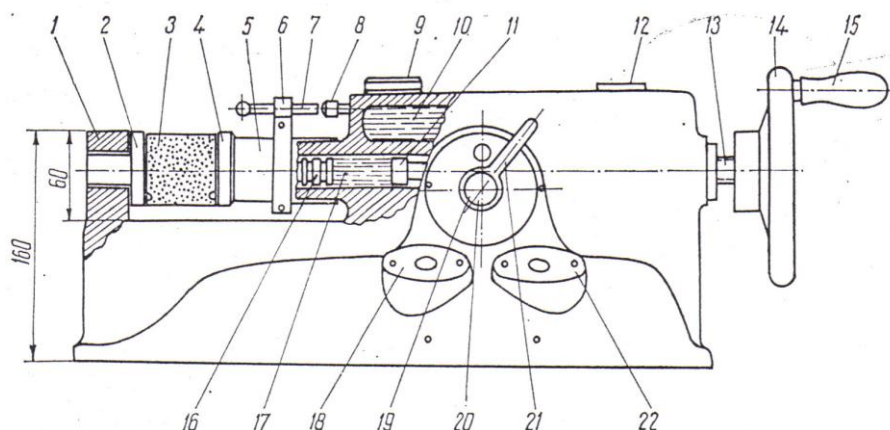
Aparat pentru încercări mecanice cu acționare hidraulică : 1-corpul aparatului ; 2-disc de sprijin ; 3-epruvetă cilindrică ; 4-disc disc de presare ; 5-piston exterior ; 6-brășară ; 7-tijă ; 8-tijă mobilă ; 9-comparator ; 10-rezervor de ulei ; 11-piston interior ; 12-dop ; 13- tija filetată ; 14-roată de mână ; 15-mâner ; 16-etanșarea pistonului exterior ; 17-cilindru ; 18-manometrul H ; 19-robinet cu trei căi ; 20-indicator ; 21-mâner ; 22-manometrul L.
